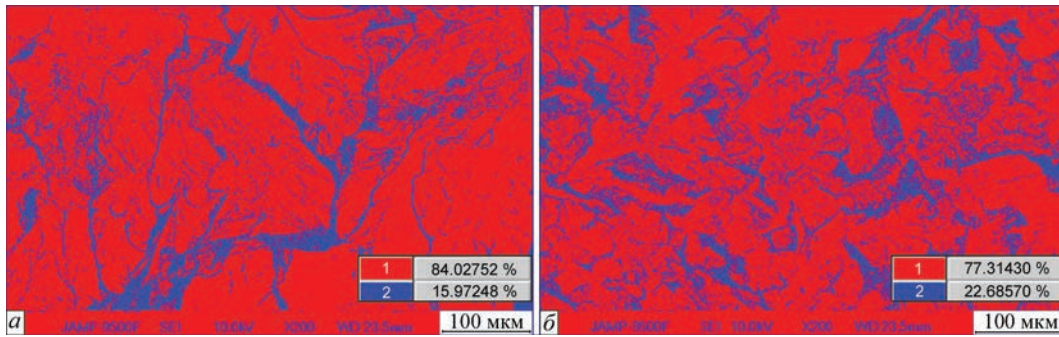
Вязкая составляющая поверхности излома сварного соединения литого (а) и деформированного (б) металла рельсовой стали ЭШП: 1 — хрупкая составляющая; 2 — вязкая
